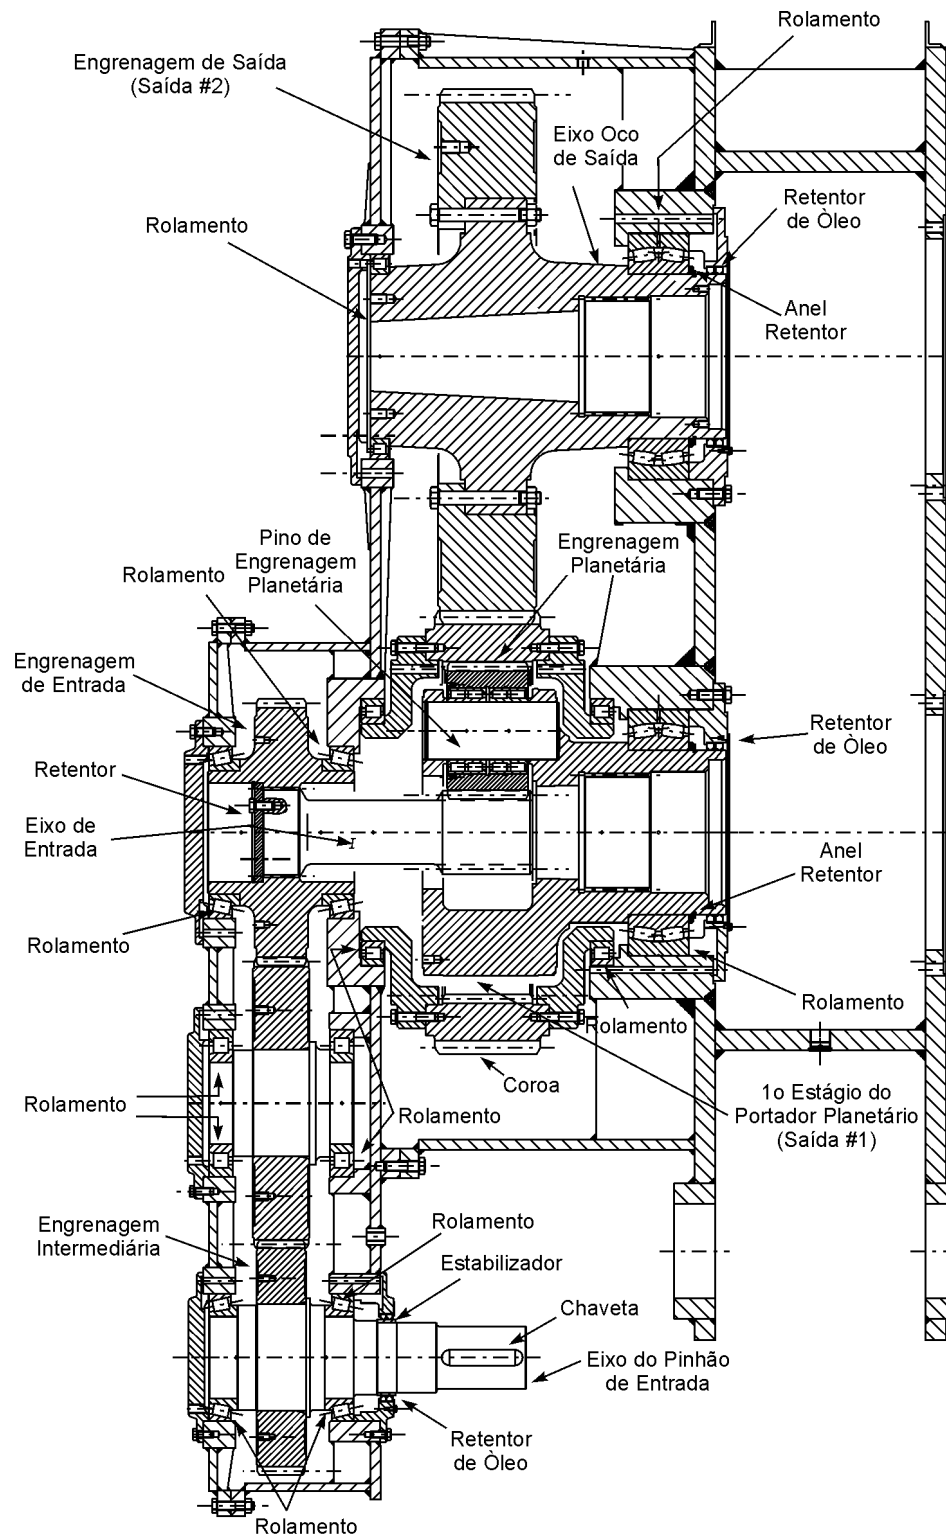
Vista da Seção da Caixa de Engrenagens de Elevação
